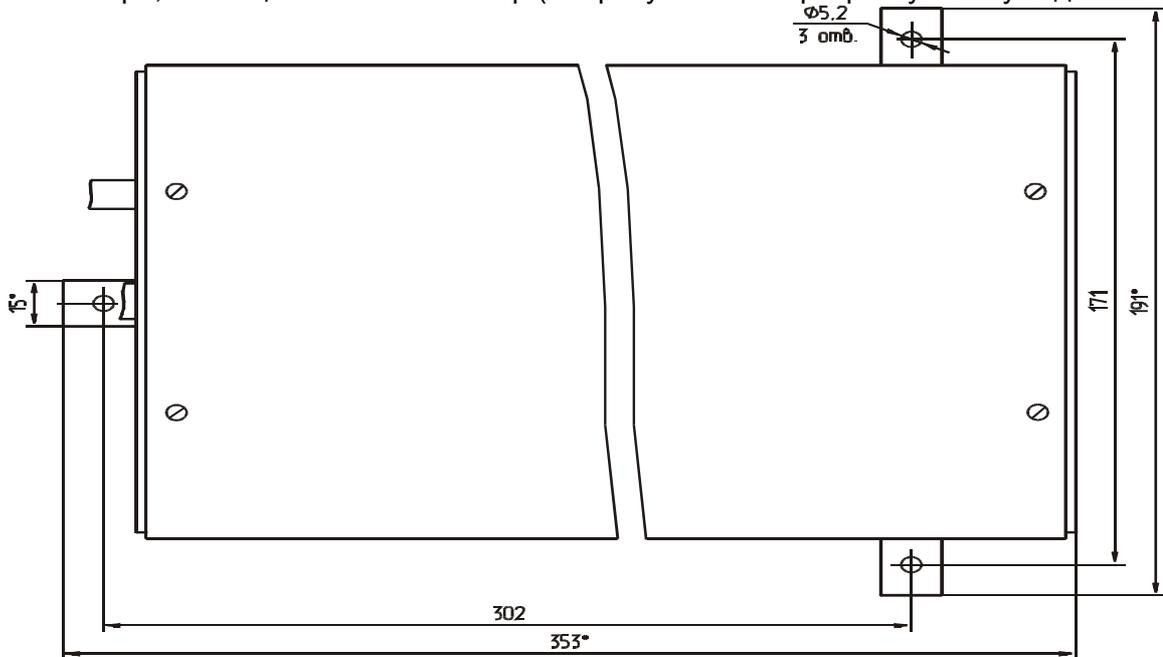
Габаритные и присоединительные размеры БПВРа
